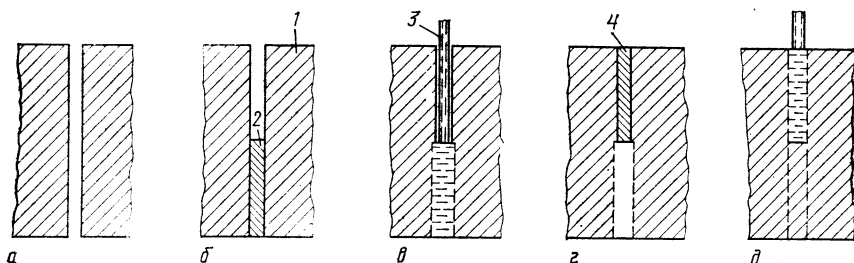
Сварка в узкую разделку [1]:
